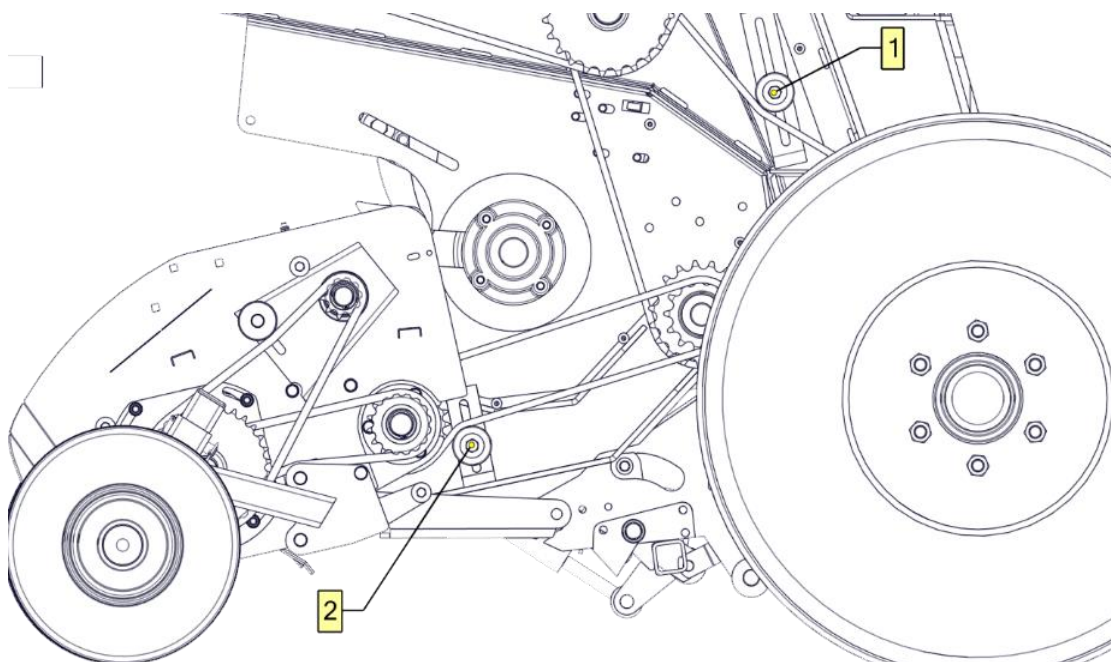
Регулировка натяжения цепей подборщика с левой стороны пресс-подборщика
